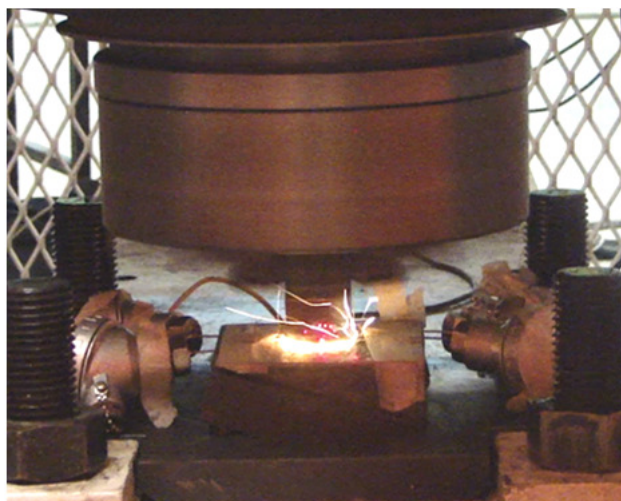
Surgimento da rebarba durante a soldagem.
